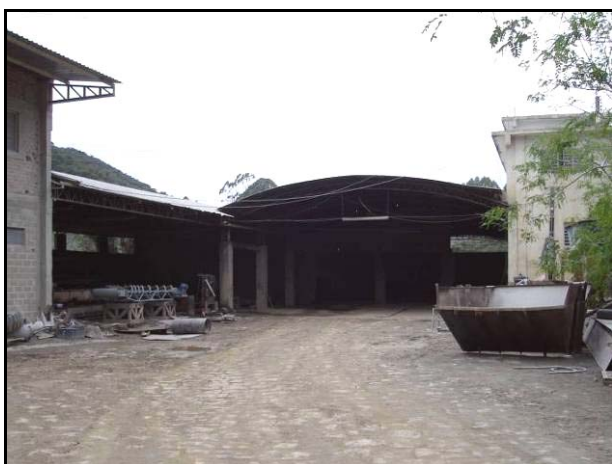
Oficina mecânica da HORICAL.
